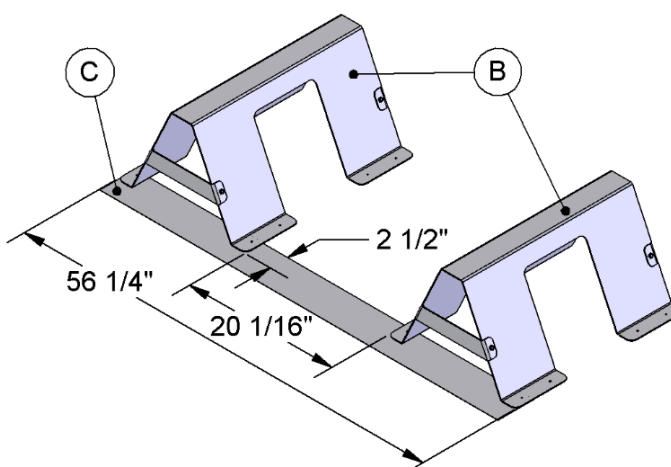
DISPOSITION ET INSTALLATION DES ESPACEURS INFÉRIEUR ET DU CAISSON INFÉRIEUR
